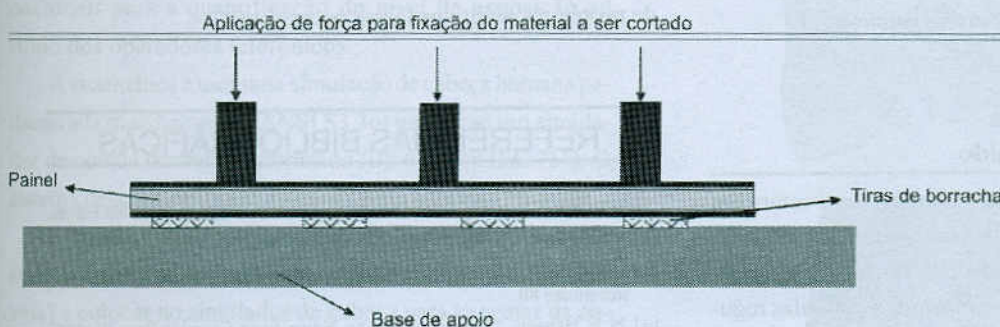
Fixação e amortecimento da estrutura a ser cortada.
